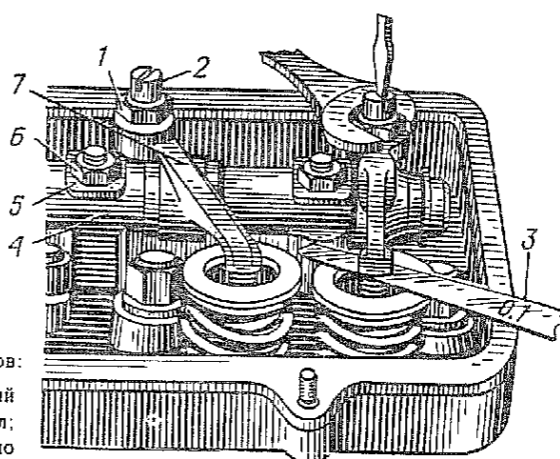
Регулировка зазоров между носками коромысел и стержнями клапанов:
